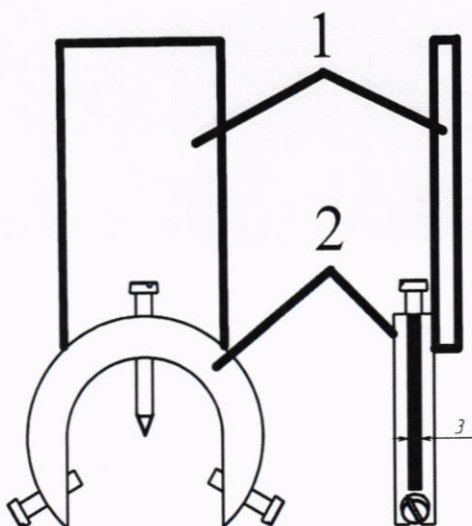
Приспособление для поверки и калибровки с отражателем: 1 – отражатель, 2 – приспособление
